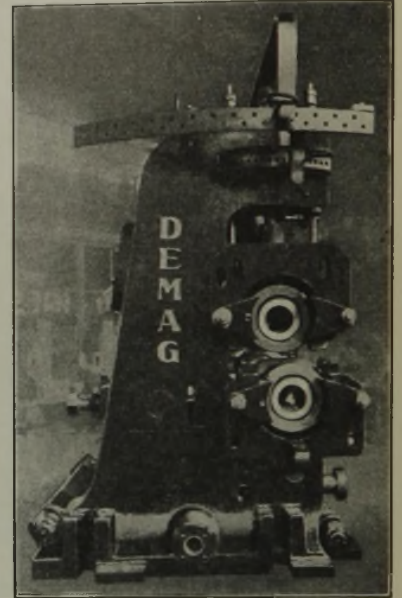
Walzgerüst mit einseitigen Ständern.
